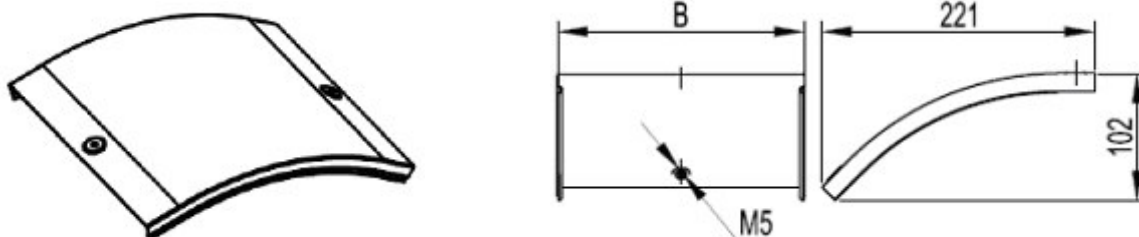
Крышка CD 45 на угол вертикальный внешний 45°
